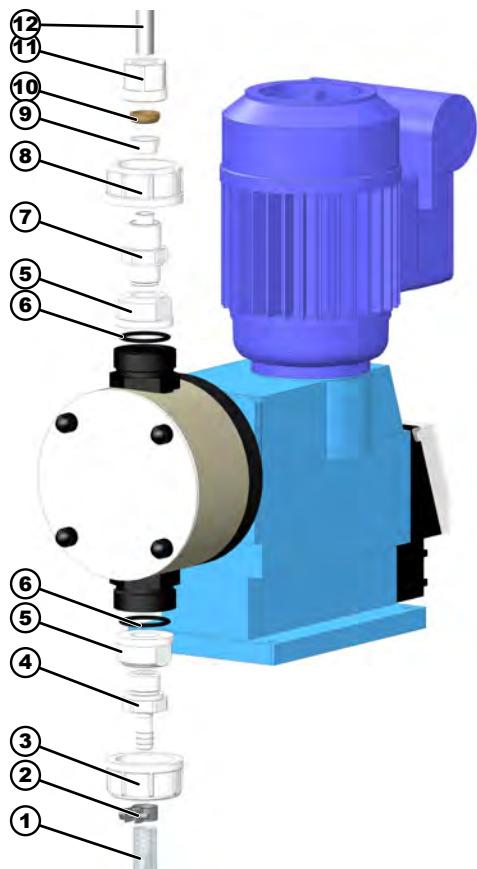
Montage Pumpenanschlussset EMP III Pumpe 80
